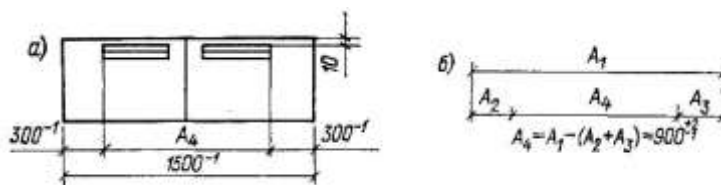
Схема сварного изделия (а) и его размерной цепи (б)
